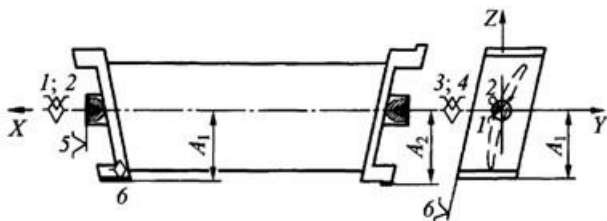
схема базування статорної лопатки при фрезеруванні профілю пера.
